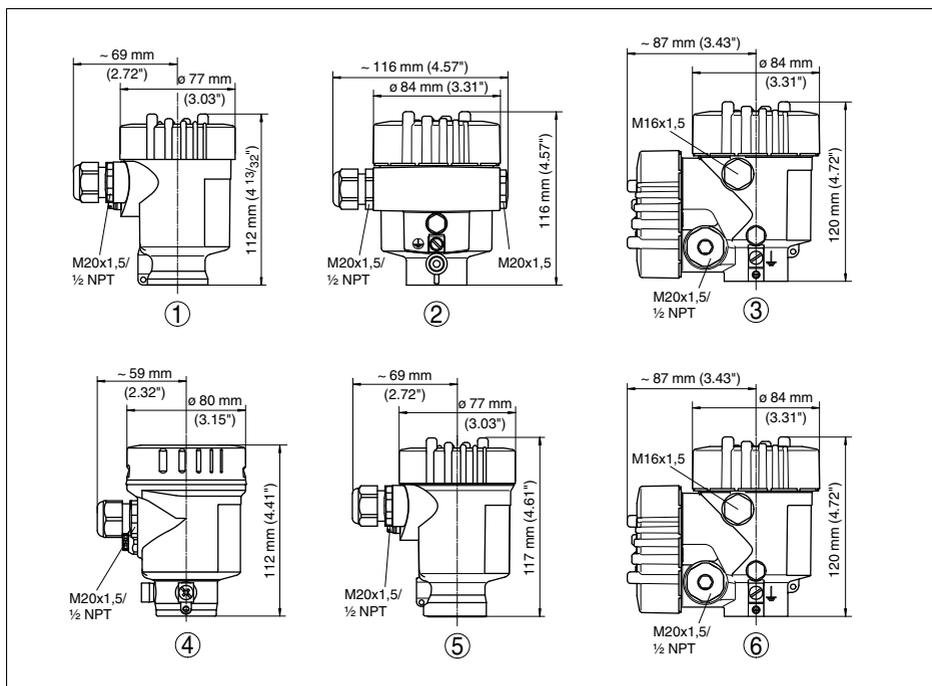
Корпуса в исполнении IP 66/IP 68 (0,2 bar) - с установленным модулем индикации и настройки корпус выше на 9 mm/0.35 in
